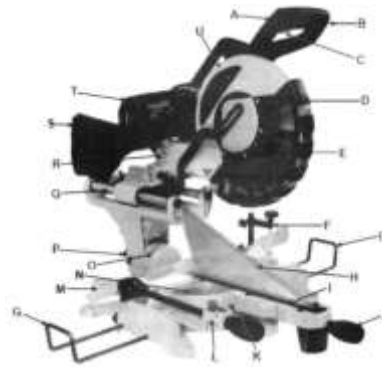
Торцювальна пила UTOOL UMS-12L:
